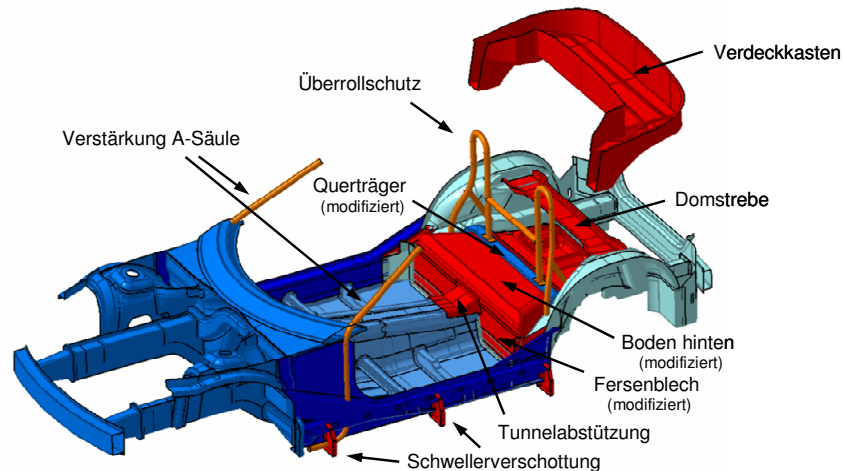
Ableitung Roadster, modifizierte und addierte Bauteile.
